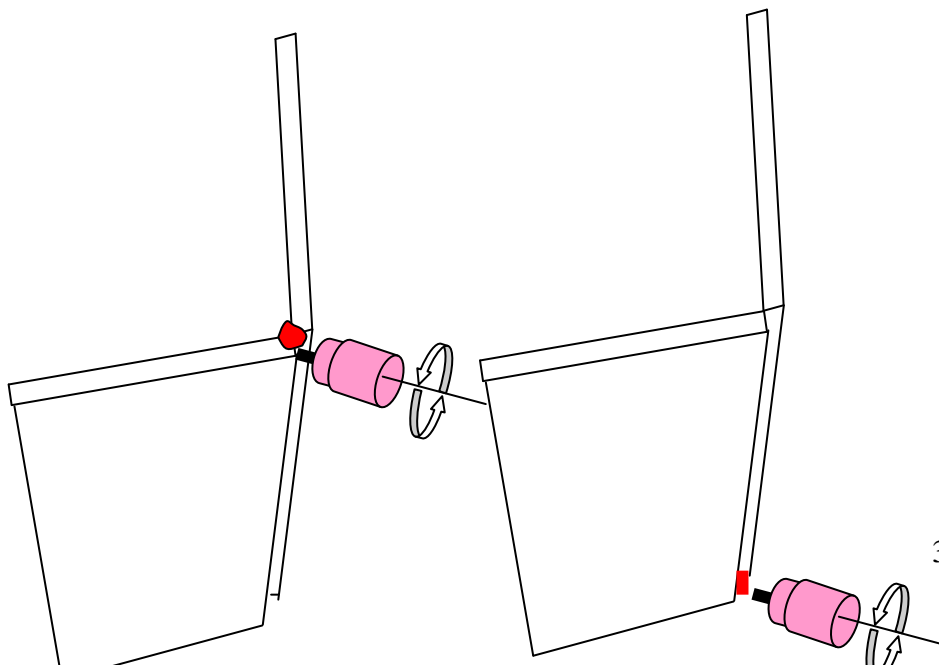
Punteado de las placas para lograr el ensamble a soldar.
